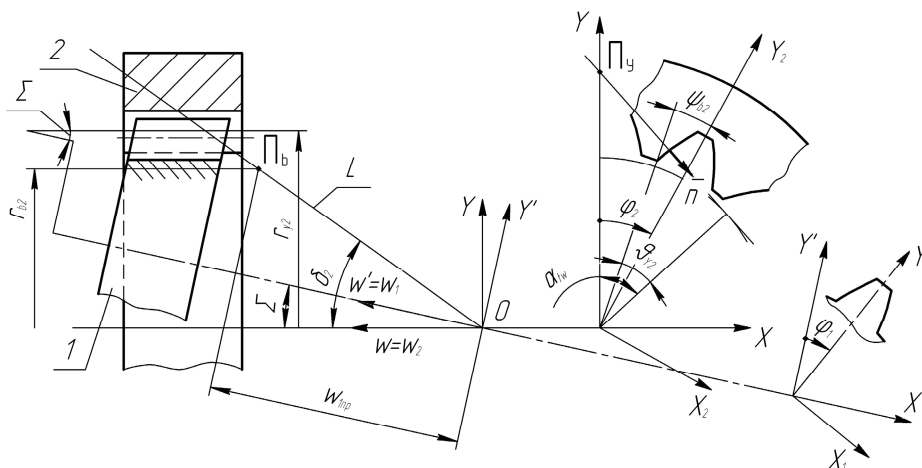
Станочное зацепление производящего колеса (2) и конической шестерни (1)
